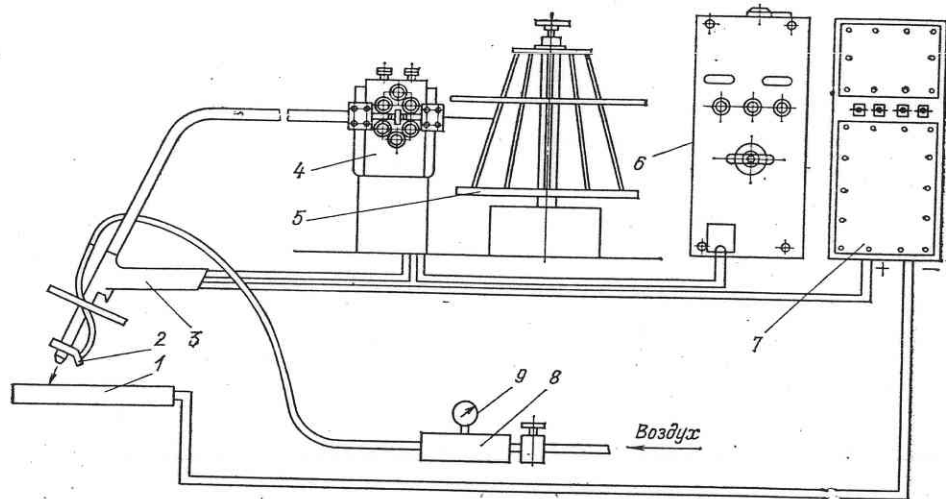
Комплект аппаратуры и оснастки для полуавтоматической строжки (резки) металла:
